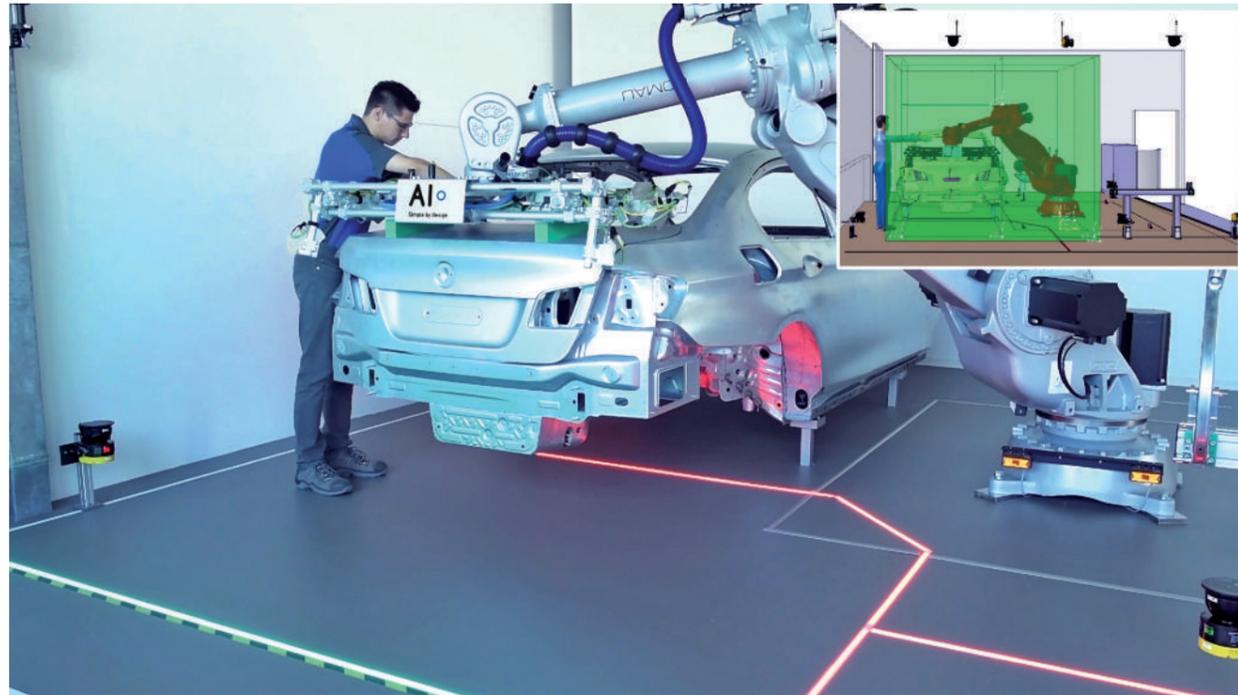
| Komplexe Mensch- Maschine- Montagelösung mittels AI Sensortechnik.
